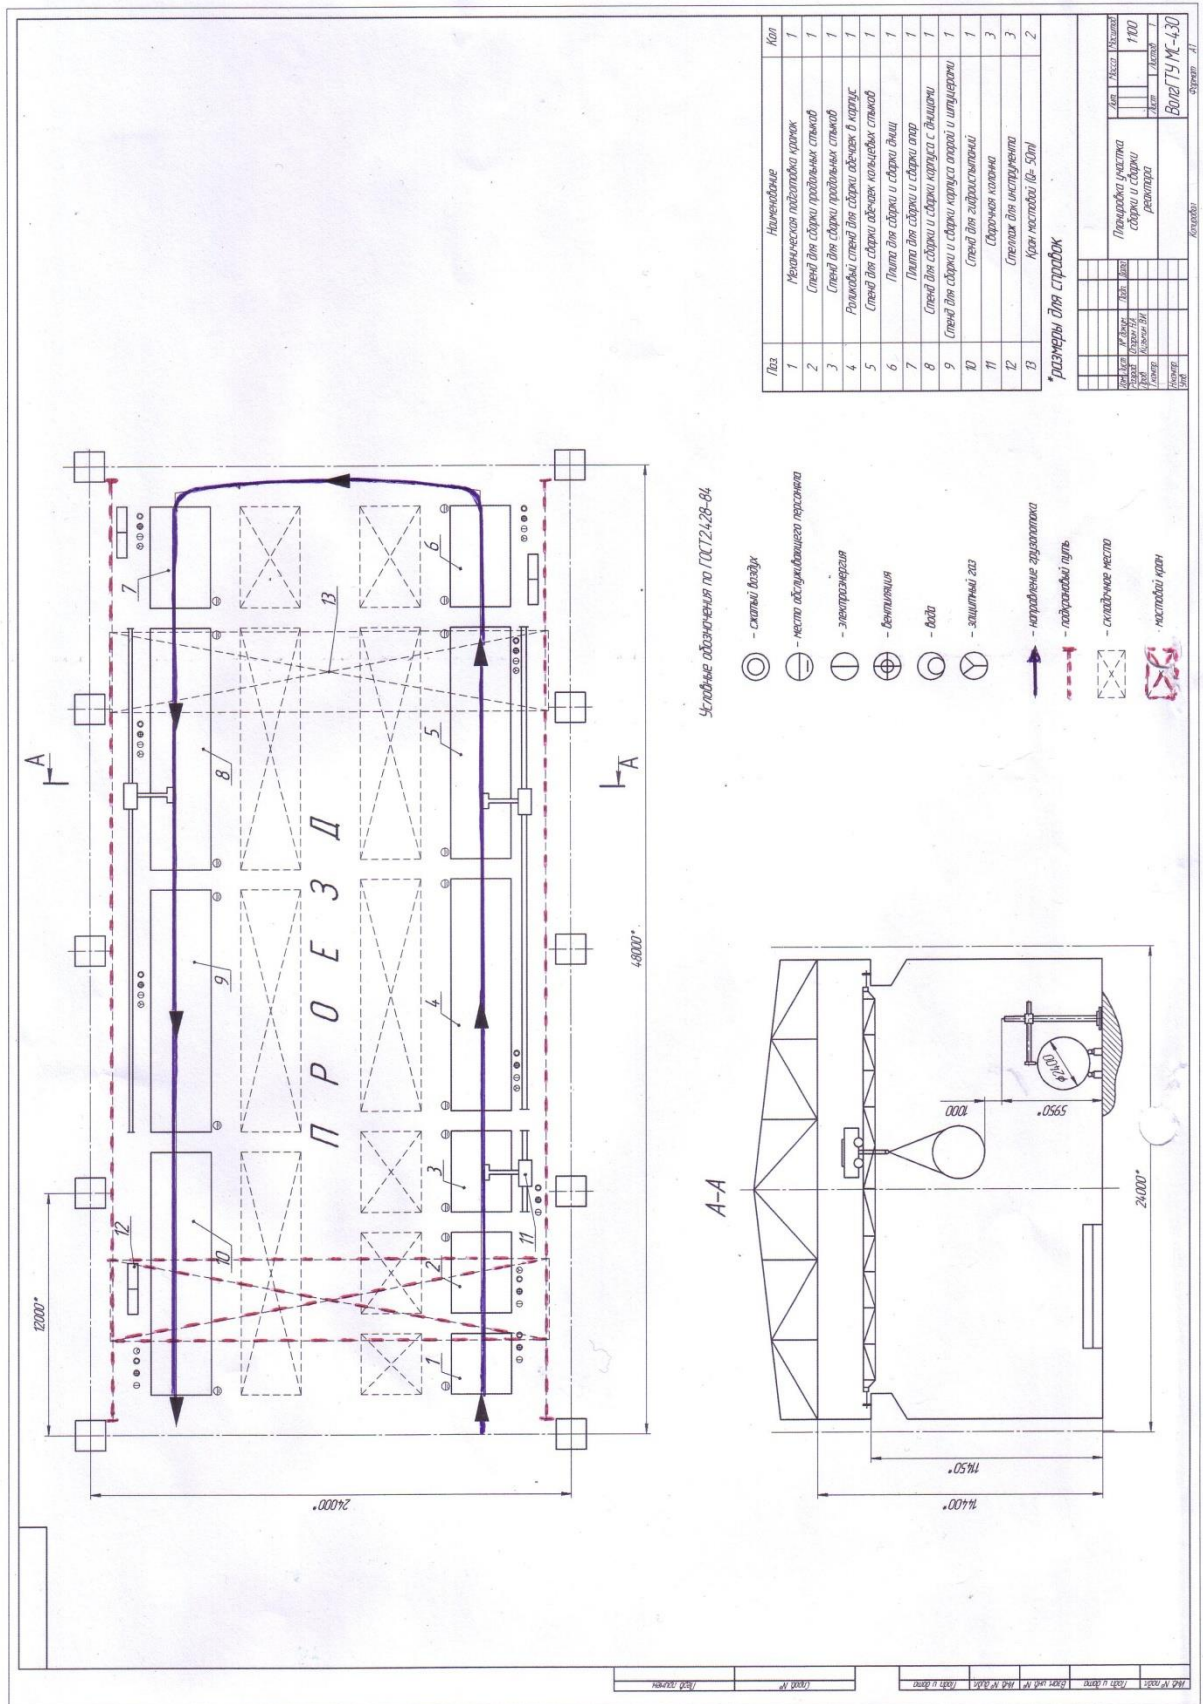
Пример планировки участка сборки и сварки реактора
